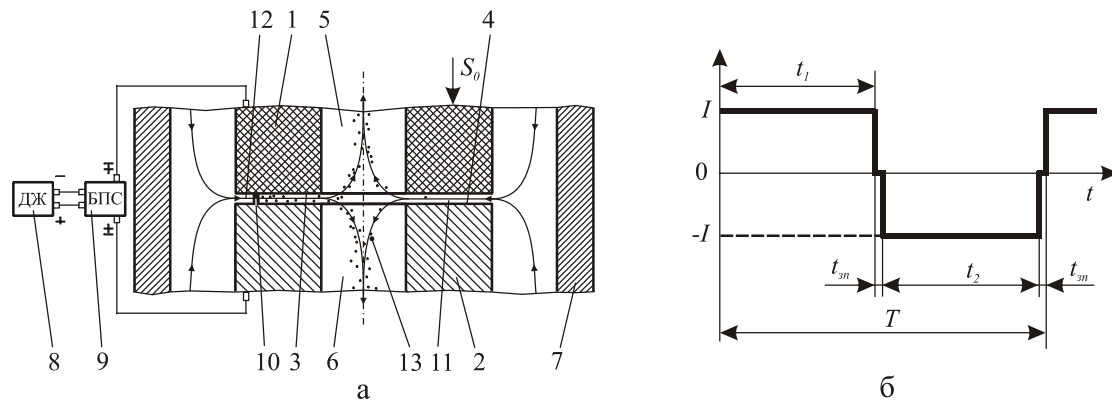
Технологічна схема формоутворення, що пропонується для обробки твердосплавного валка: а - схема; б - типовий графік режиму роботи біполярного перетворювача сили технологічного струму; 1, 2 - валки, що обробляються; 3, 4 - торцеві поверхні валків; 5, 6 - центральні отвори у валках; 7 - герметизована камера; 8 - джерело живлення постійним технологічним струмом; 9 - біполярний перетворювач струму; 10 - електрична дуга; 11 - торцевий міжелектродний зазор; 12 - гідродинамічний потік; 13 - продукти ерозії
